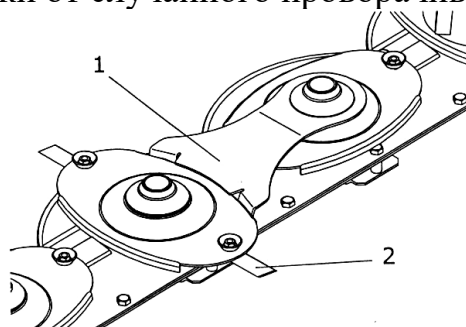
Крепление ножа (режущий аппарат с быстросъемными ножами)
